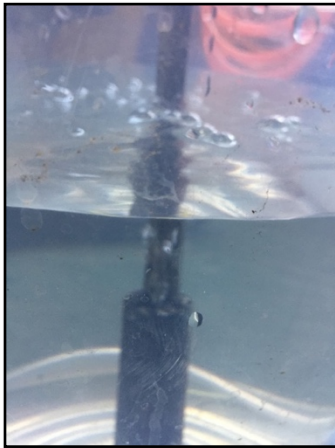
Prueba de estanqueidad de la soldadura
